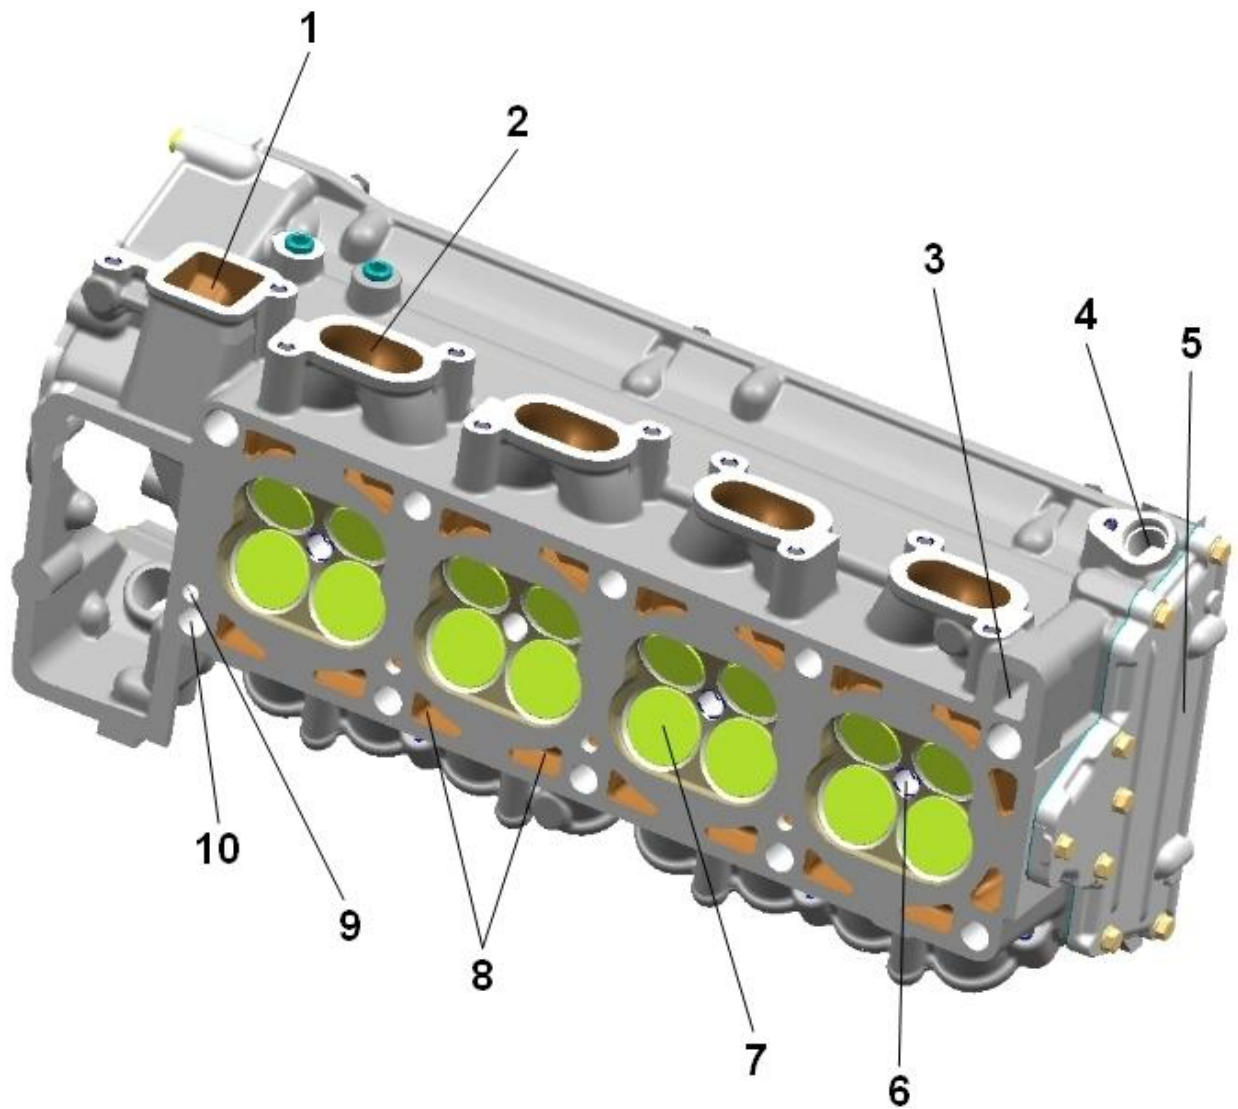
Головка цилиндров. Вид на камеры сгорания, фланец выпускного коллектора и заднюю крышку:
